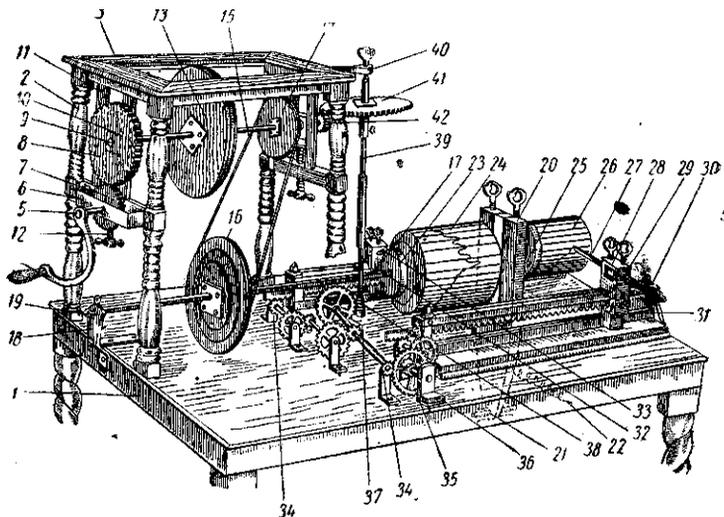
Кинематическая схема токарно-копировального станка 1712 г.
